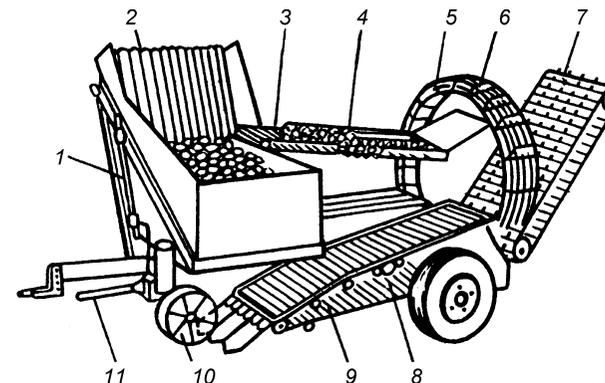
Основная система картофелекопателя-подборщика [378]: 1 — гидравлический опрокидывающий механизм; 2 — бункер; 3 — транспортер переборщик; 4 — дисковая сортировка; 5 — вспомогательный механизм-отделитель; 6 — подъемное колесо; 7 — ботвоотводящий элеватор; 8 — встряхивающая решетка; 9 — прутковый элеватор; 10 — гребневой каток; 11 — привод от вала отбора мощности
